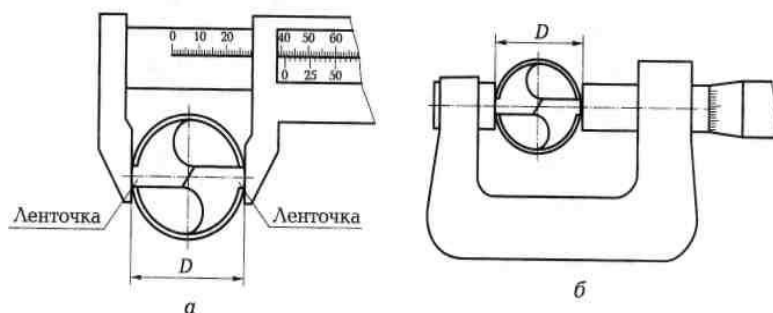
Схемы измерения диаметра сверла штангенциркулем (а) и микрометром (б)
